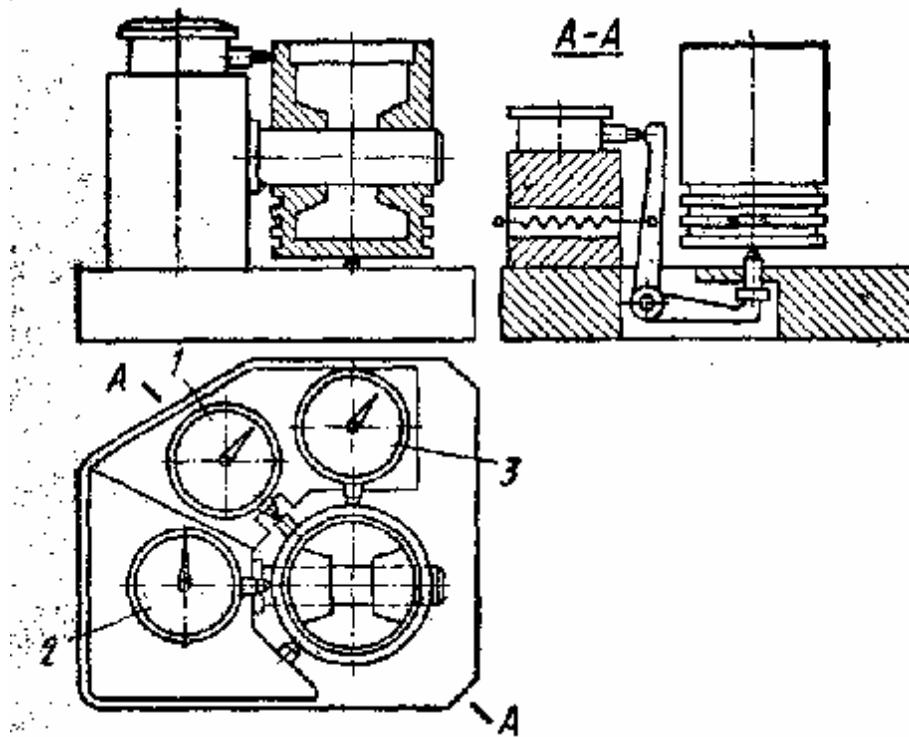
Схема багатовимірного контрольного пристосування для перевірки поршня
